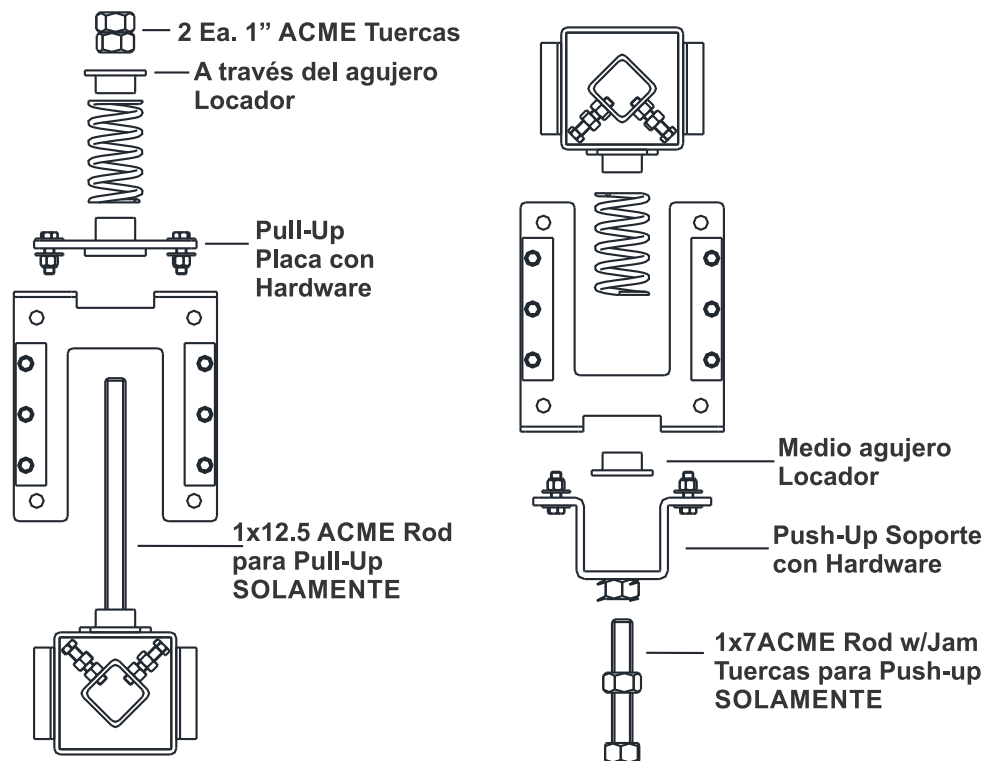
Duo-Spring conjunto tensor: Pull-Up (izquierda) y Push-Up (derecha) Tensor
